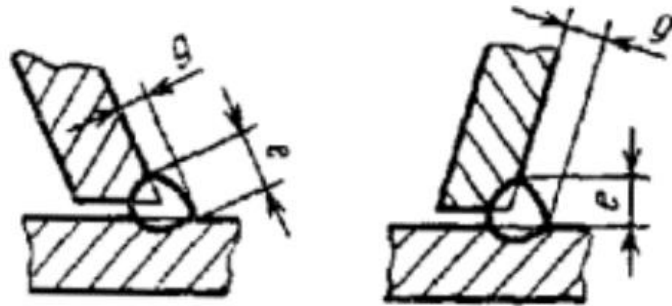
Схема зварного шва згідно з ГОСТ 23518-79
